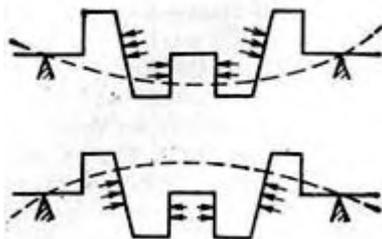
Схема правки коленчатого вала местным наклепом.
